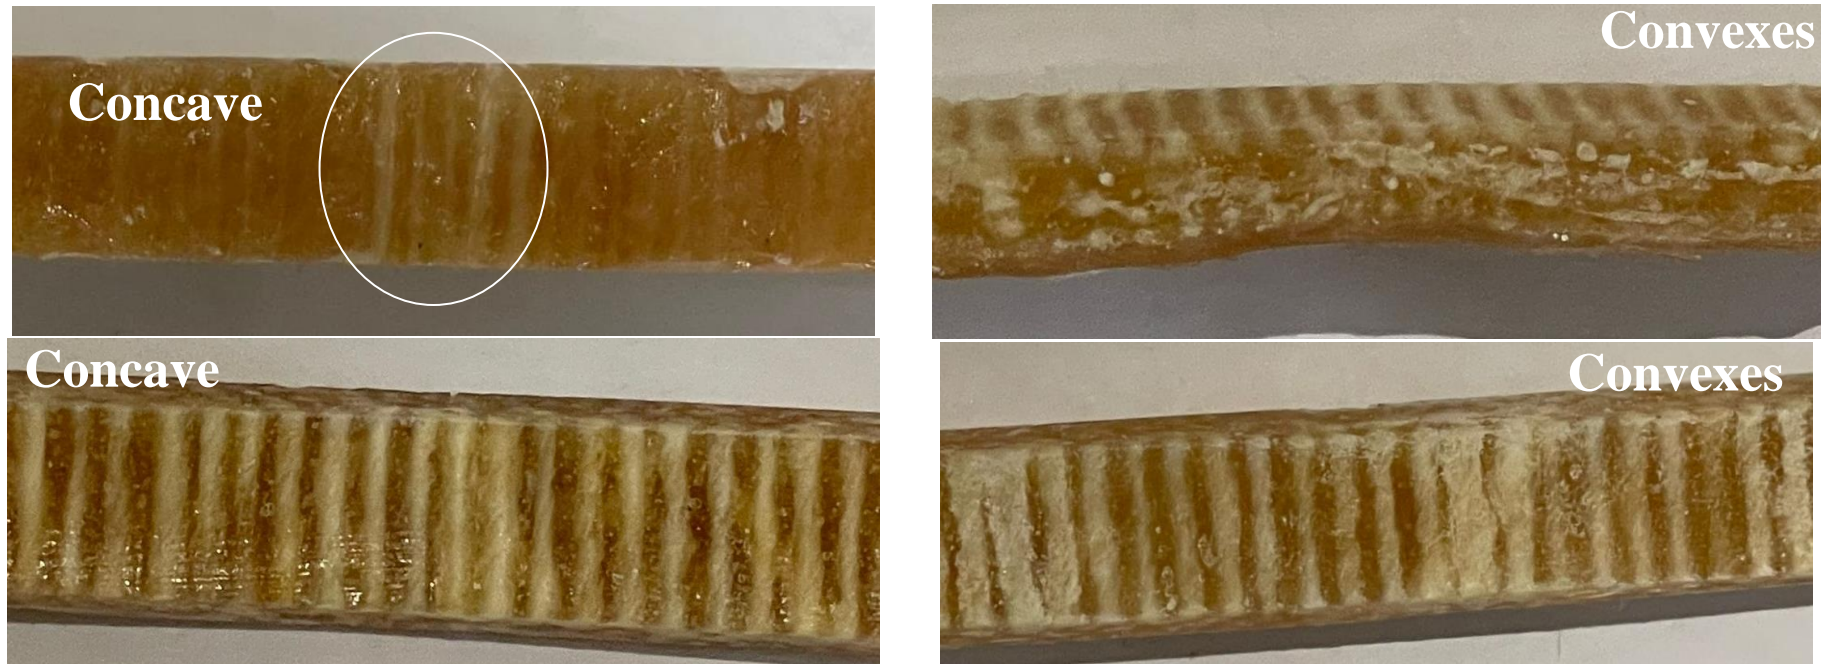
Faciès de rupture des éprouvettes concave (éprouvette 1), convexe (éprouvette 3) testées en flexion 3-points).
